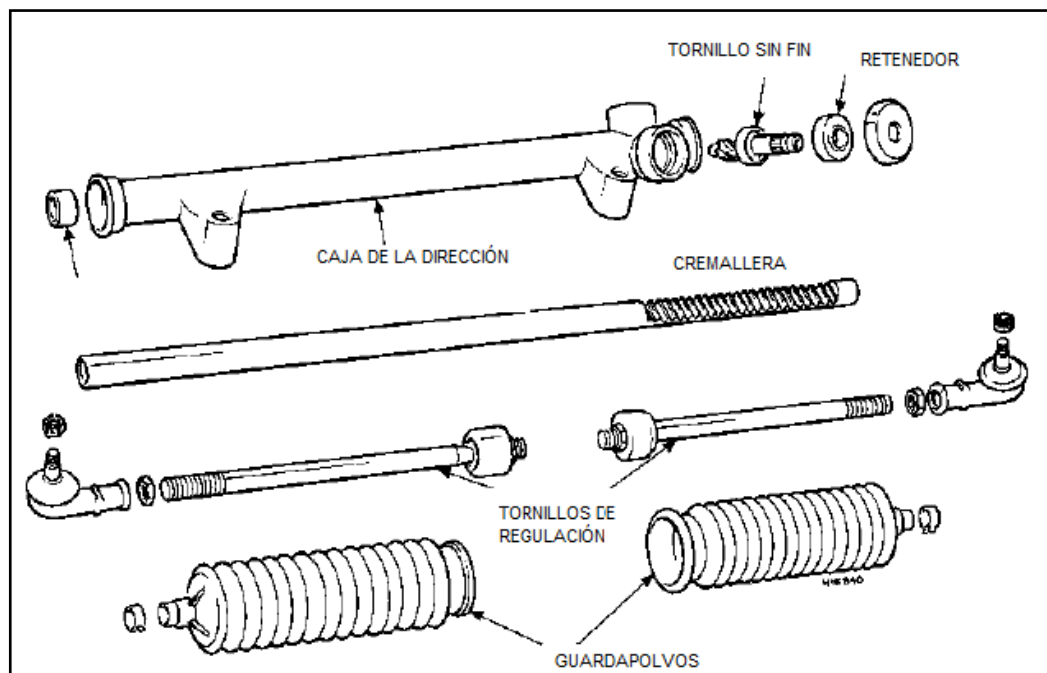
Despiece del Sistema de Dirección por Cremallera
